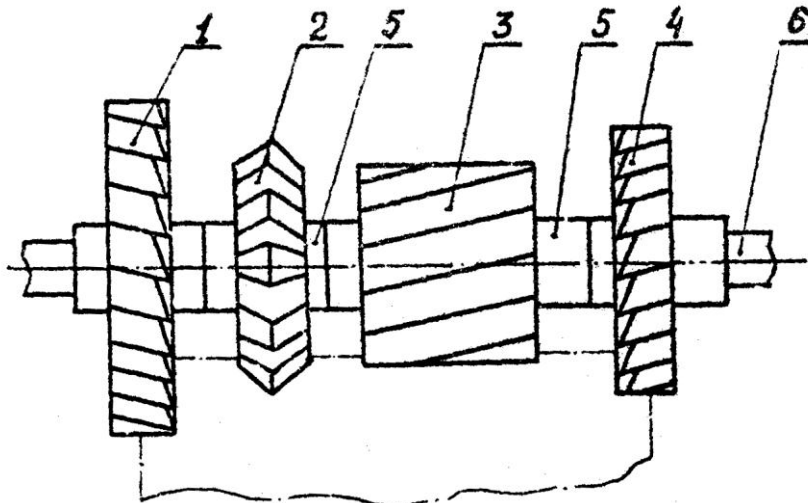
Блок фрез: 1, 2, 3, 4 – набор фрез; 5 – установочные кольца; 6 – оправка
